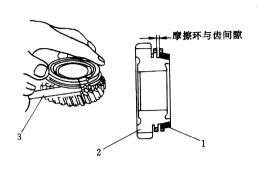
同步环与齿轮端面间隙的检查 1. 同步环 2. 齿轮 3. 塞尺
